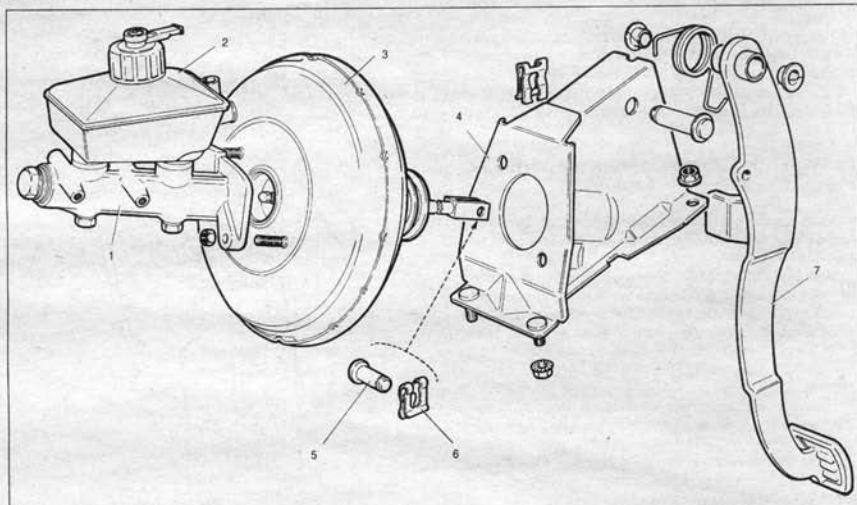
Детали крепления вакуумного усилителя и главного цилиндра:
